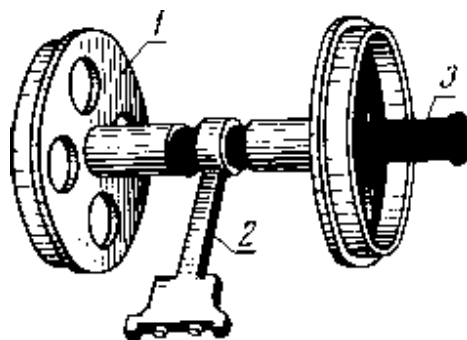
Пристосування КИ-7093 для установки вторинного валу коробки передач трактора ДТ-75М:
